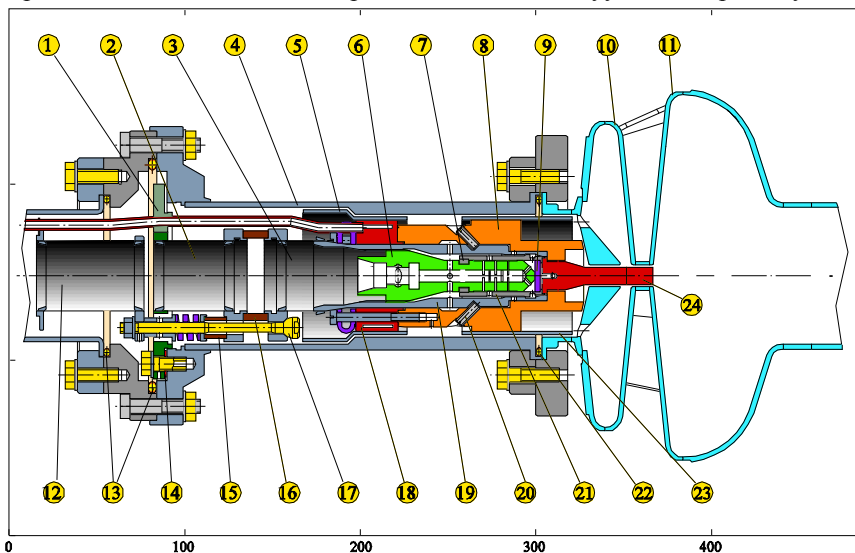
Фотокатодная ВЧ пушка со сверхпроводящим резонатором: 1 - фланец крепления катодного узла к корпусу (4); 2, 3 - тонкостенные трубы из нержавеющей стали; 4 - корпус; 5 - внутренний проводник коаксиальной линии из нержавеющей стали; 6 - винт из титана; 7 - фиксирующие полукольца; 8 - теплообменник; 9 - диск; 10 - резонатор заграждающего фильтра; 11 - ускоряющий резонатор; 12 - тонкостенная труба; 13, 22 - вакуумные уплотнения; 14 - регулировочные шайбы; 15, 16 - керамические изоляторы; 17 - винты; 18 - кулер с каналом и трубками подачи жидкого азота; 19 - патрон с внутренней резьбой; 20 - винты; 21 - стаканчик с припаянным к нему стержнем (24); 23 - внутренний проводник коаксиальной линии из нержавеющей стали; 24 - катодный стержень.
